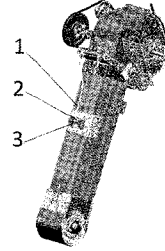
Элеватор колосовой с домолачивающим устройством: 1 – тяга; 2, 3 – гайки
